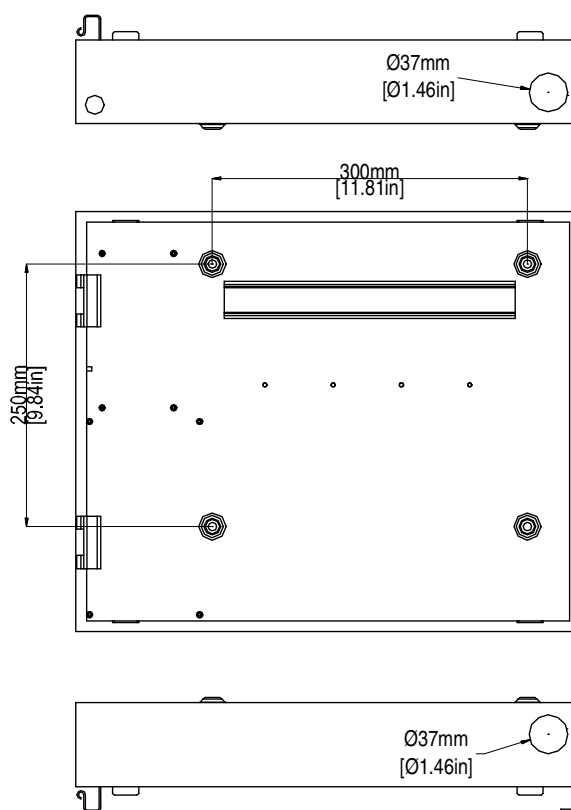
Vista interna y plantilla de perforación para la fijación a la pared
